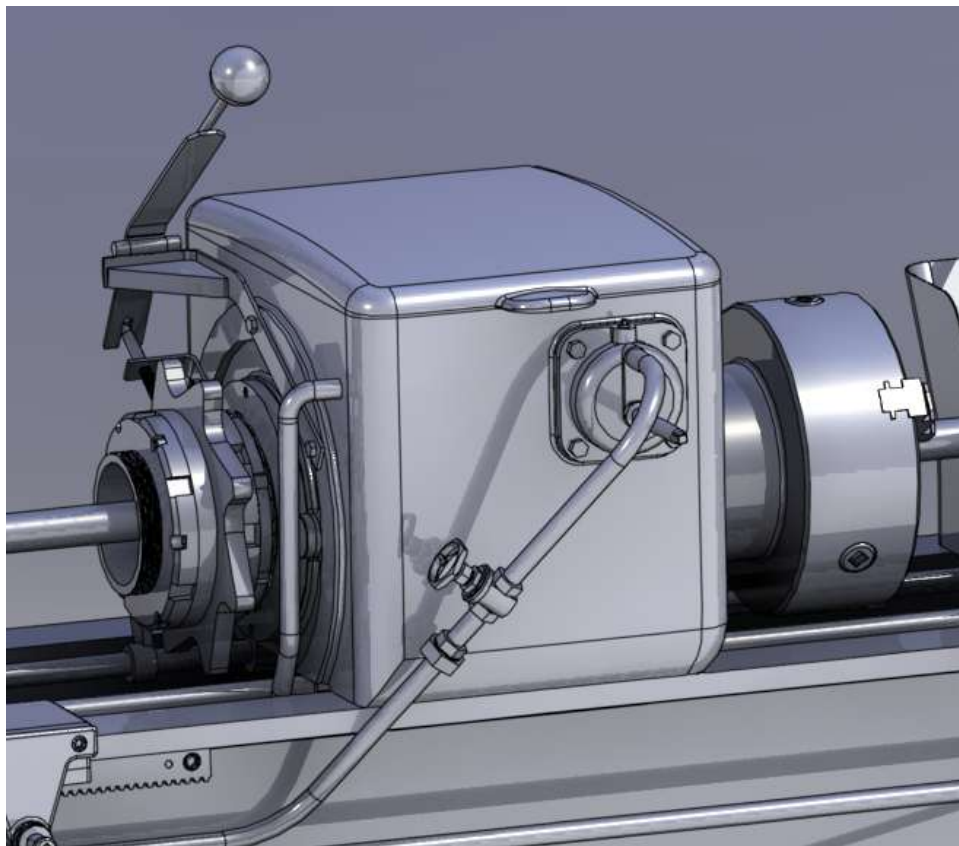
Detail vizualizace sestavy suportu Zs 151
